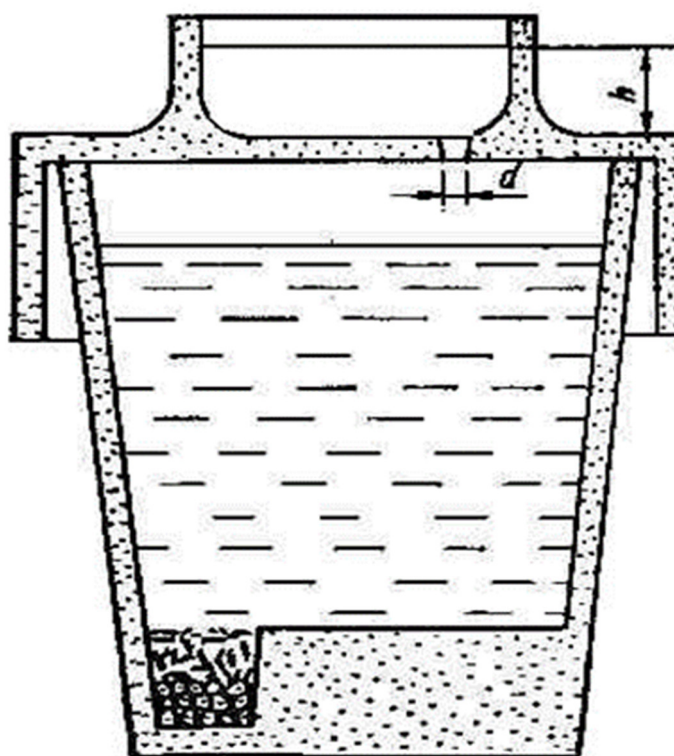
Схема ковша со съёмной крышкой – чашей
